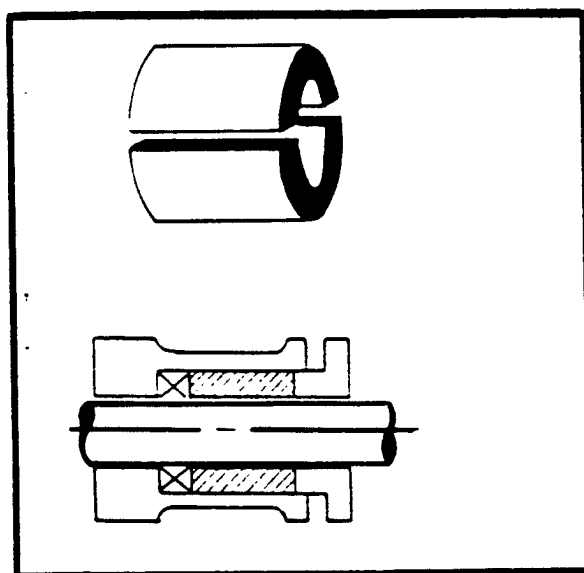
Instalación de empaquetaduras metálicas y plásticas
